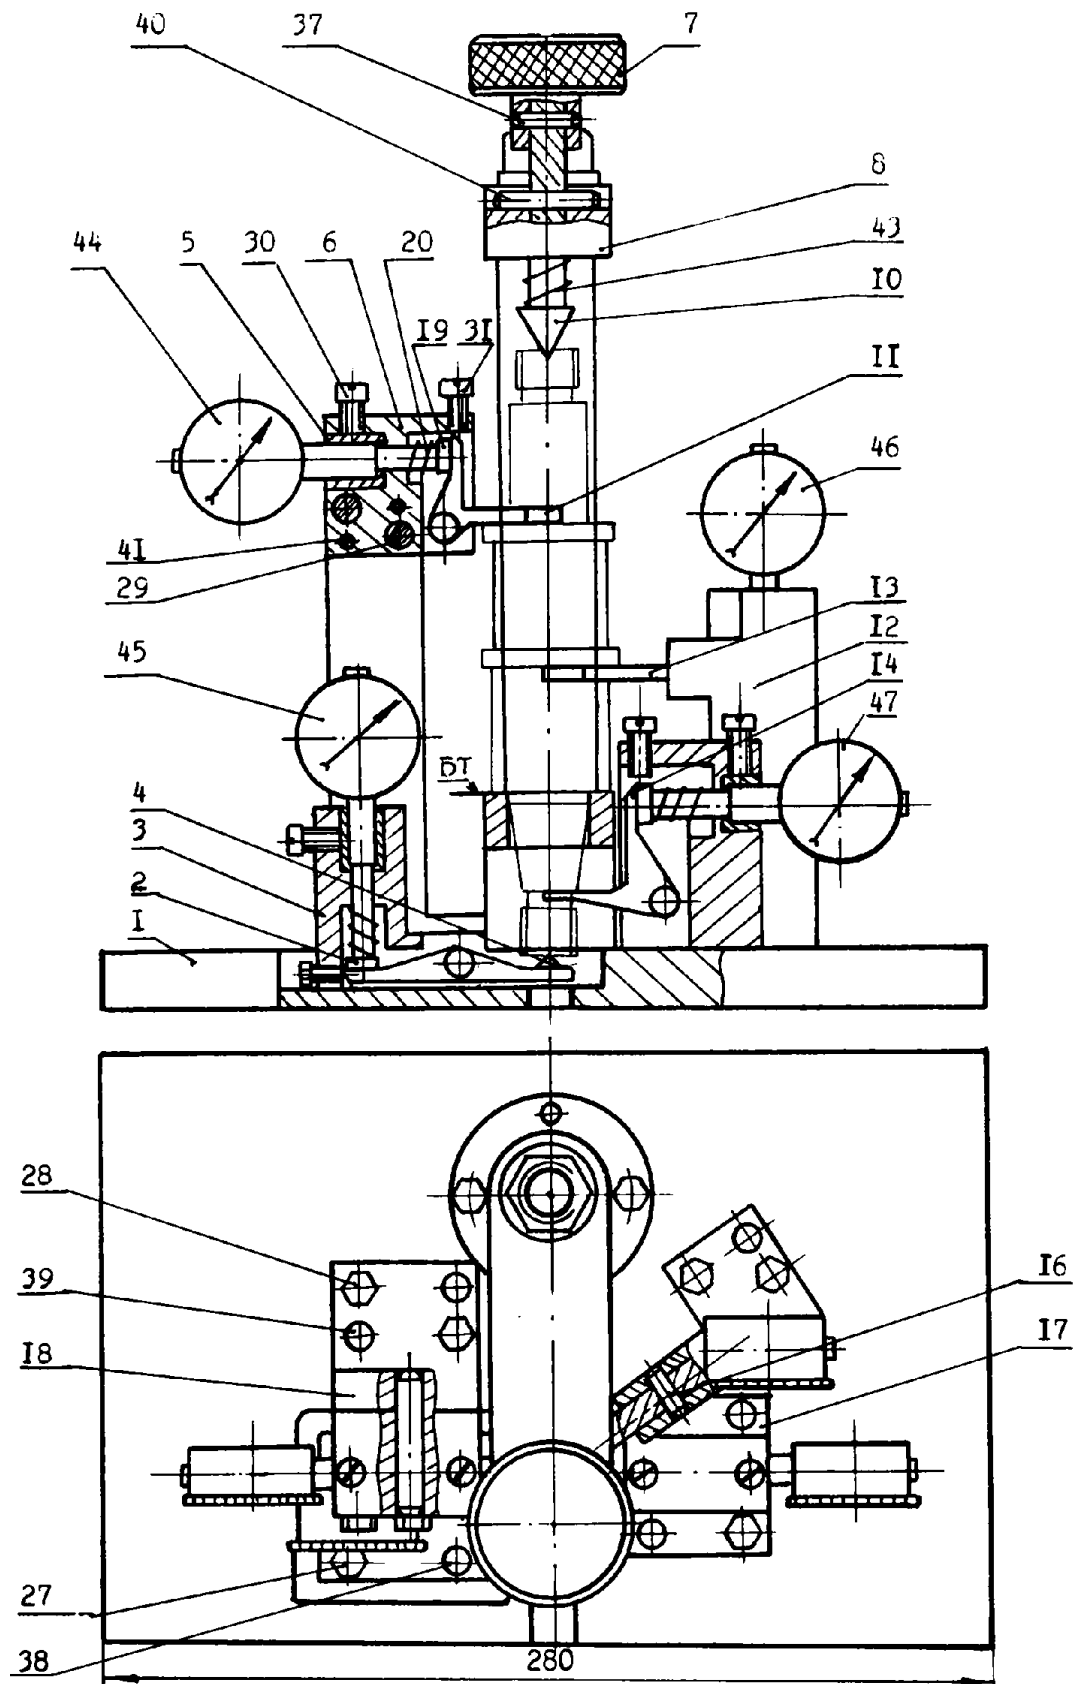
б – Багатомірний пристрій для контролю лінійного розташування шийок валів
